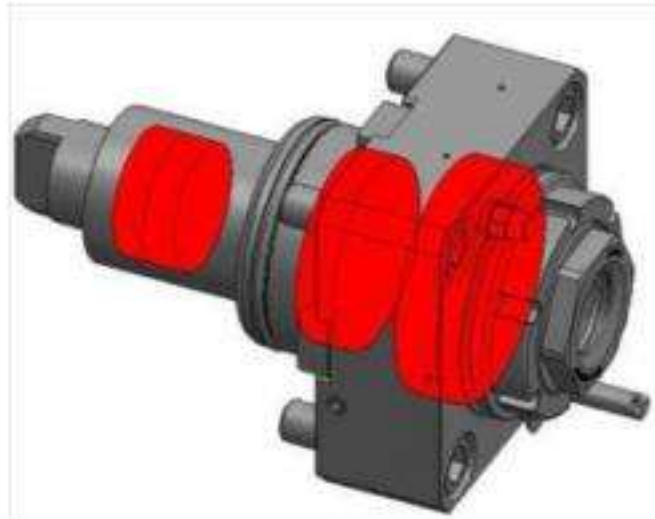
Конструкція підшипників кочення в блоках для приводного інструмента за стандартом BMT[3]
